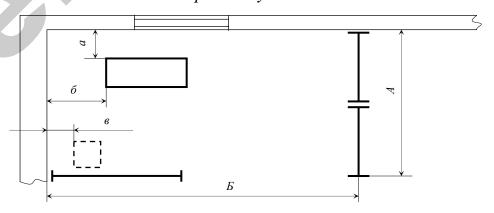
Нормы расстановки оборудования на сварочном участке
